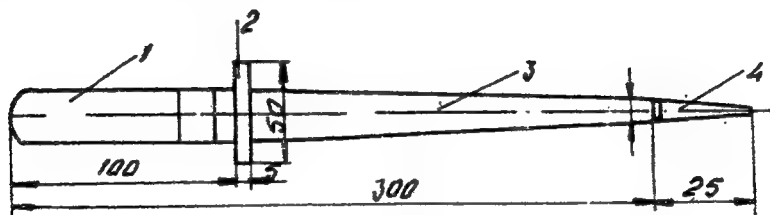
Testerul (ștanga) pentru măsurarea rezistenței de izolație: 1 - mineral izolant; 2 - opritorul; 3 - partea izolantă; 4 - vârful metalic asamblat prin înșurubare.
